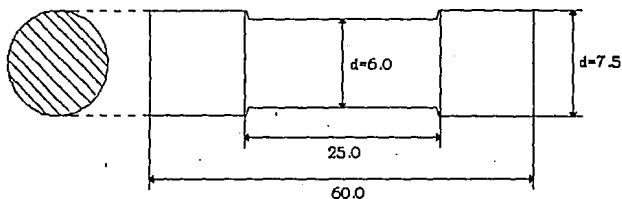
Dimensiones de la probeta para ensayos de tracción en una Máquina Universal Instron
